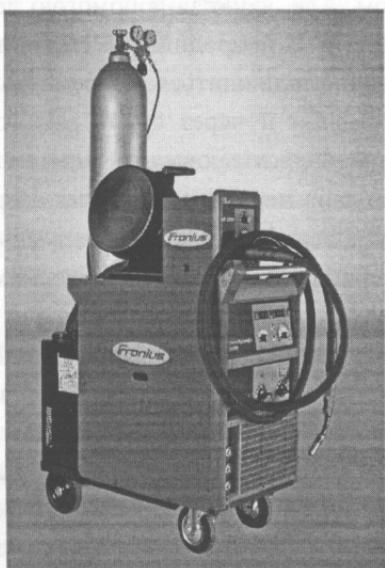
Загальний вигляд апарату VarioSynergic 5000/5000-2 для напівавтоматичного зварювання у вуглекислому газі
